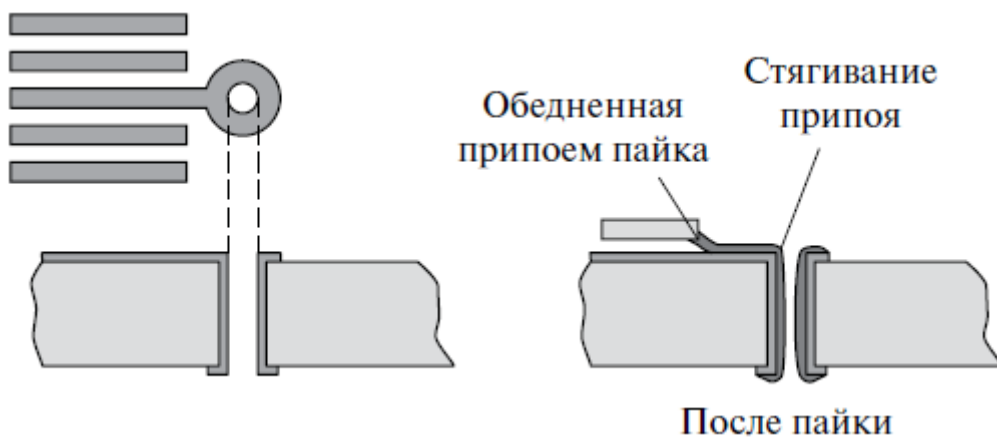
Отток припоя с монтажной площадки в металлизированное отверстие
